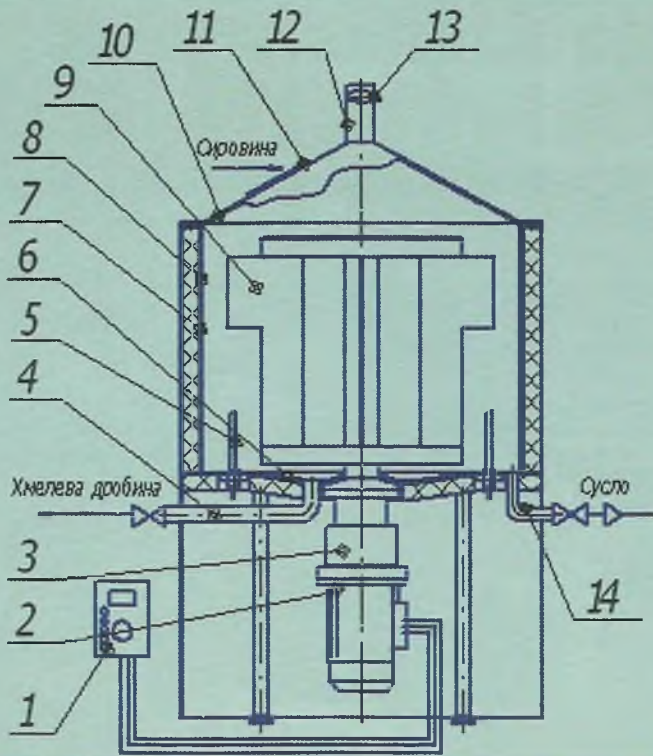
Схема комбінованого апарата, розробленого на основі сусловарильного апарата фірми "Кий-пиво": 1 — частотний перетворювач; 2 — електродвигун; 3 — хвильовий редуктор; 4 — патрубок для відведення хмелевого залишку; 5 — ТЕН; 6 — днище; 7 — корпус; 8 — ізоляція; 9 — рамна мішалка; 10 — конічна кришка; 11 — вікно; 12 — труба відведення пари; 13 — шибер; 14 — патрубок відведення сушла.
